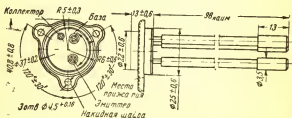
Габаритный чертёж транзисторов П209, П210А.
